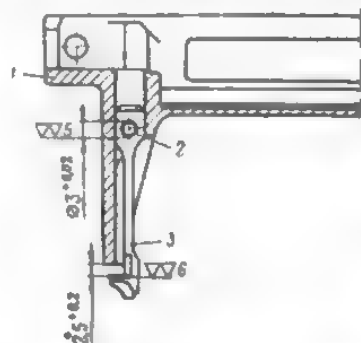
Постановка защелки скобы в ствольную коробку:
